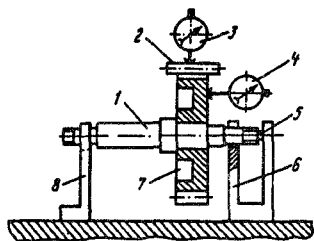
Схема контроля радиального и торцового биения сборочной единицы «зубчатое колесо — вал»
